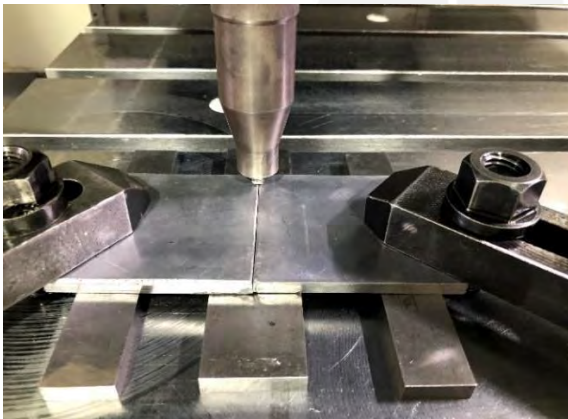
Montaje de cupones a soldar con Pin MX trivex Montaje en maquina.
